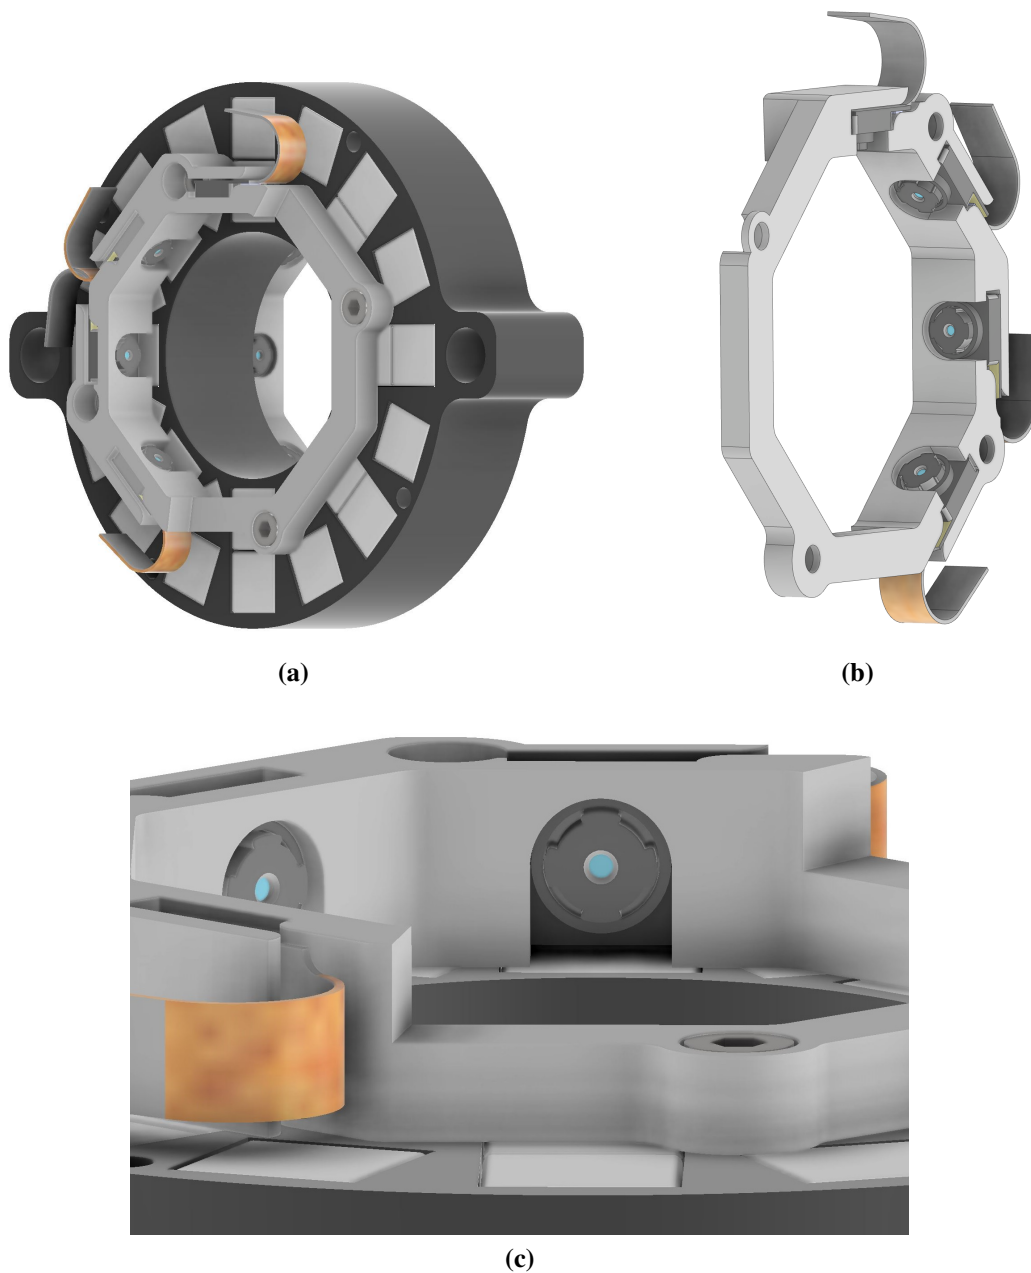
Kamerahalterung, welche direkt auf einen PMQ aufgeschraubt wird. (a) Für die Befestigung werden die Durchgangsbohrungen verwendet, mit welchen ebenfalls die Abdeckung aufgeschraubt wird. (b) Die Halterung ist zur einen Seite geöffnet, um die Kameras einzusetzen. (c) Die Halterung wird mit der offenen Seite zum PMQ gerichtet, sodass die Kameras fixiert sind.
